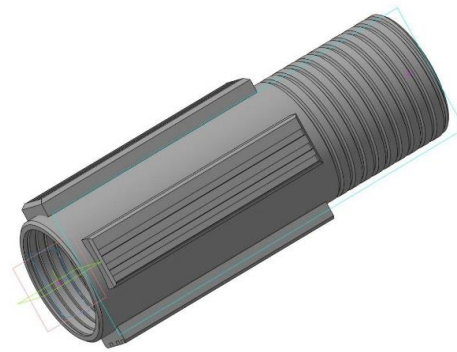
Центриатор для стабилизирующей компоновки ССК-96
